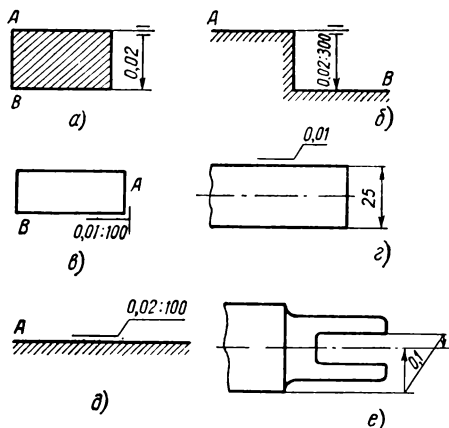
Отклонения от заданной геометрической формы и расположения поверхностей фрезерованной детали:
